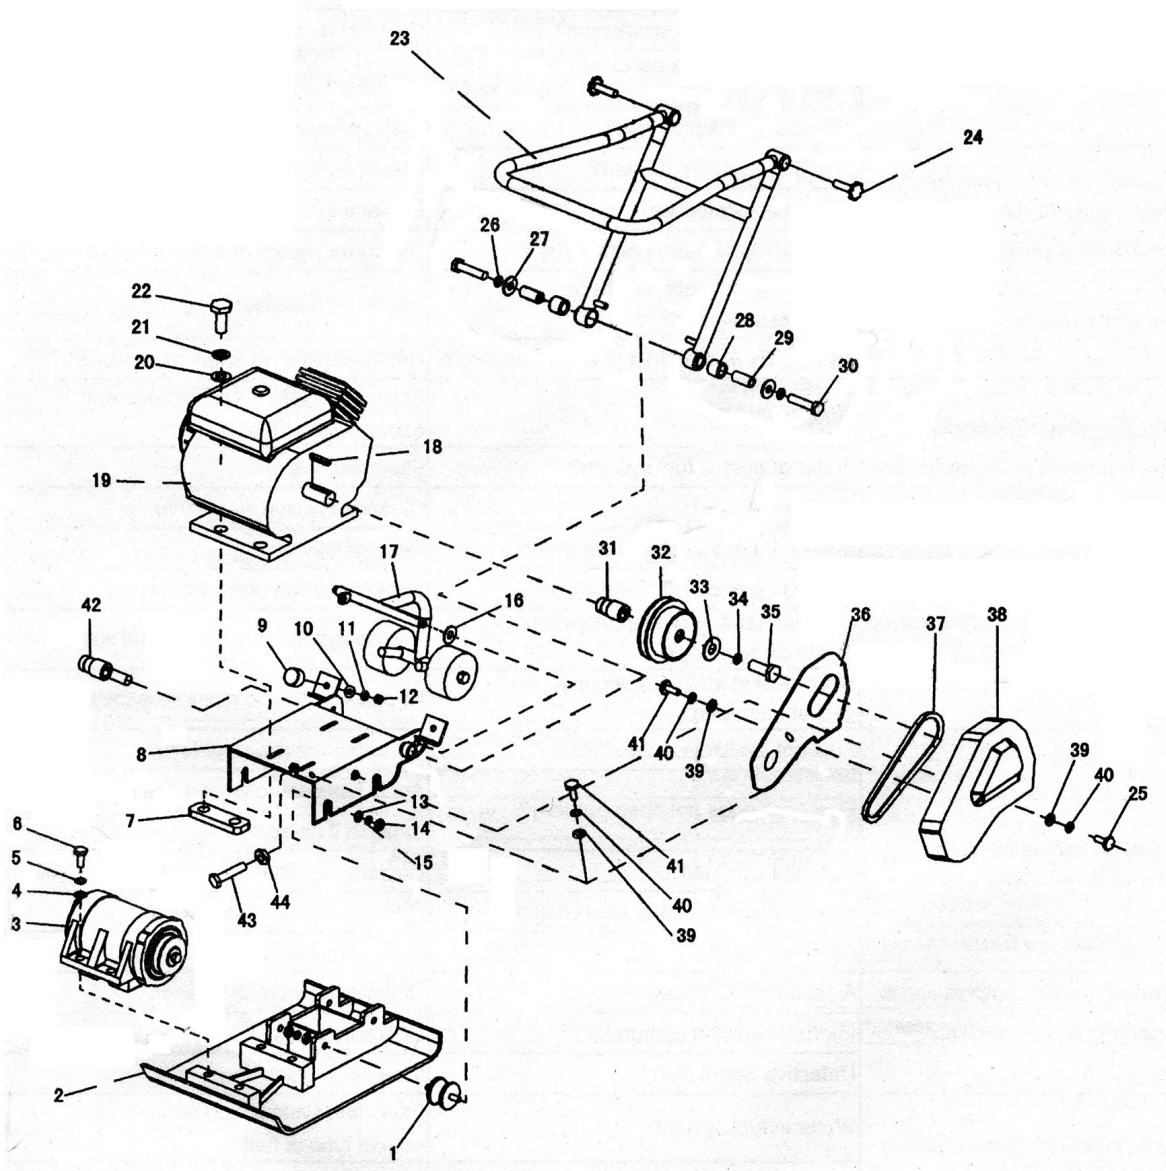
Vue éclatée de la plaque vibrante AY-460-SF H
